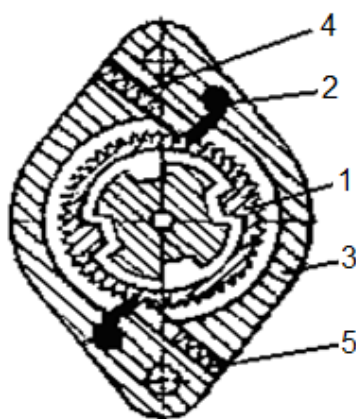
Поворотный механизм с двумя собачками в корпусе
